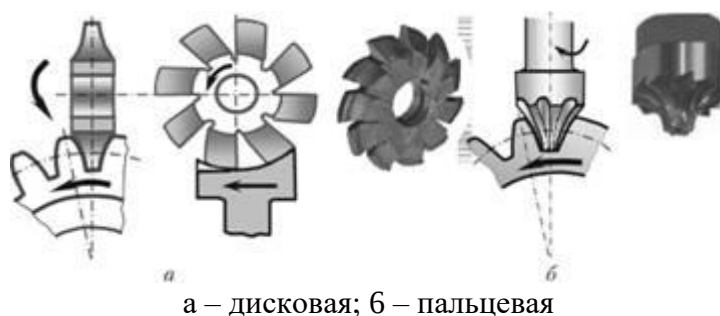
Схемы нарезания зубчатых колес модульными фрезами
